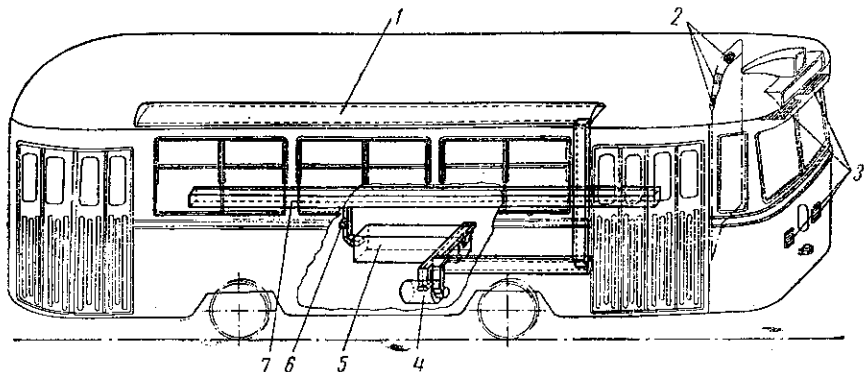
Схема вентиляции и отопления вагона КТМ-2:
